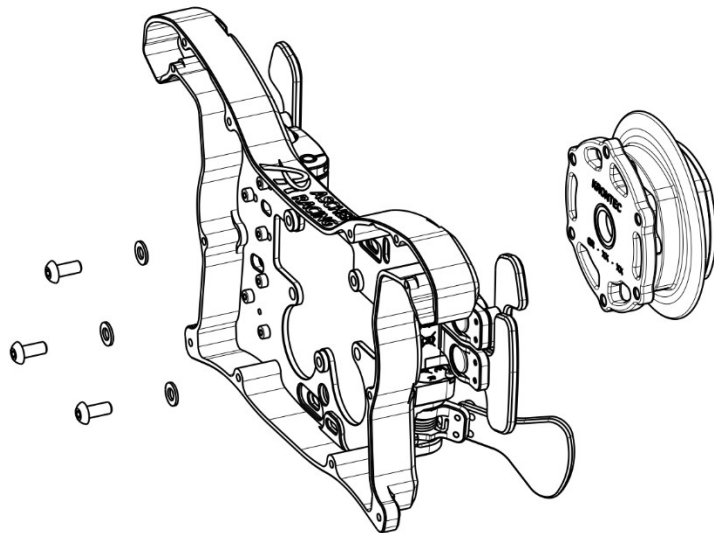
Montage eines QRs mit M5-Gewinde
